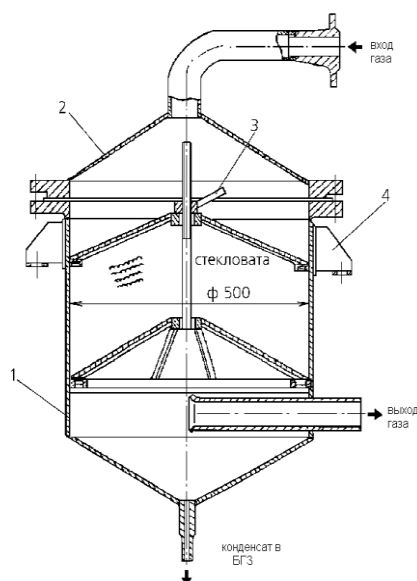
Конструкция фильтра самоочищающегося TS21(22,23)N01: 1 - корпус; 2 - крышка; 3 - рукоятка; 4 - опора
